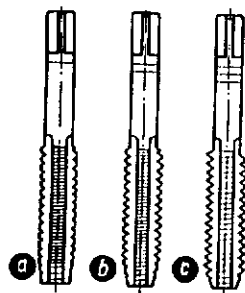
Machos de roscar a máquina. a) Macho de tallado previo; b) macho de tallado intermedio; c) macho de acabado.
